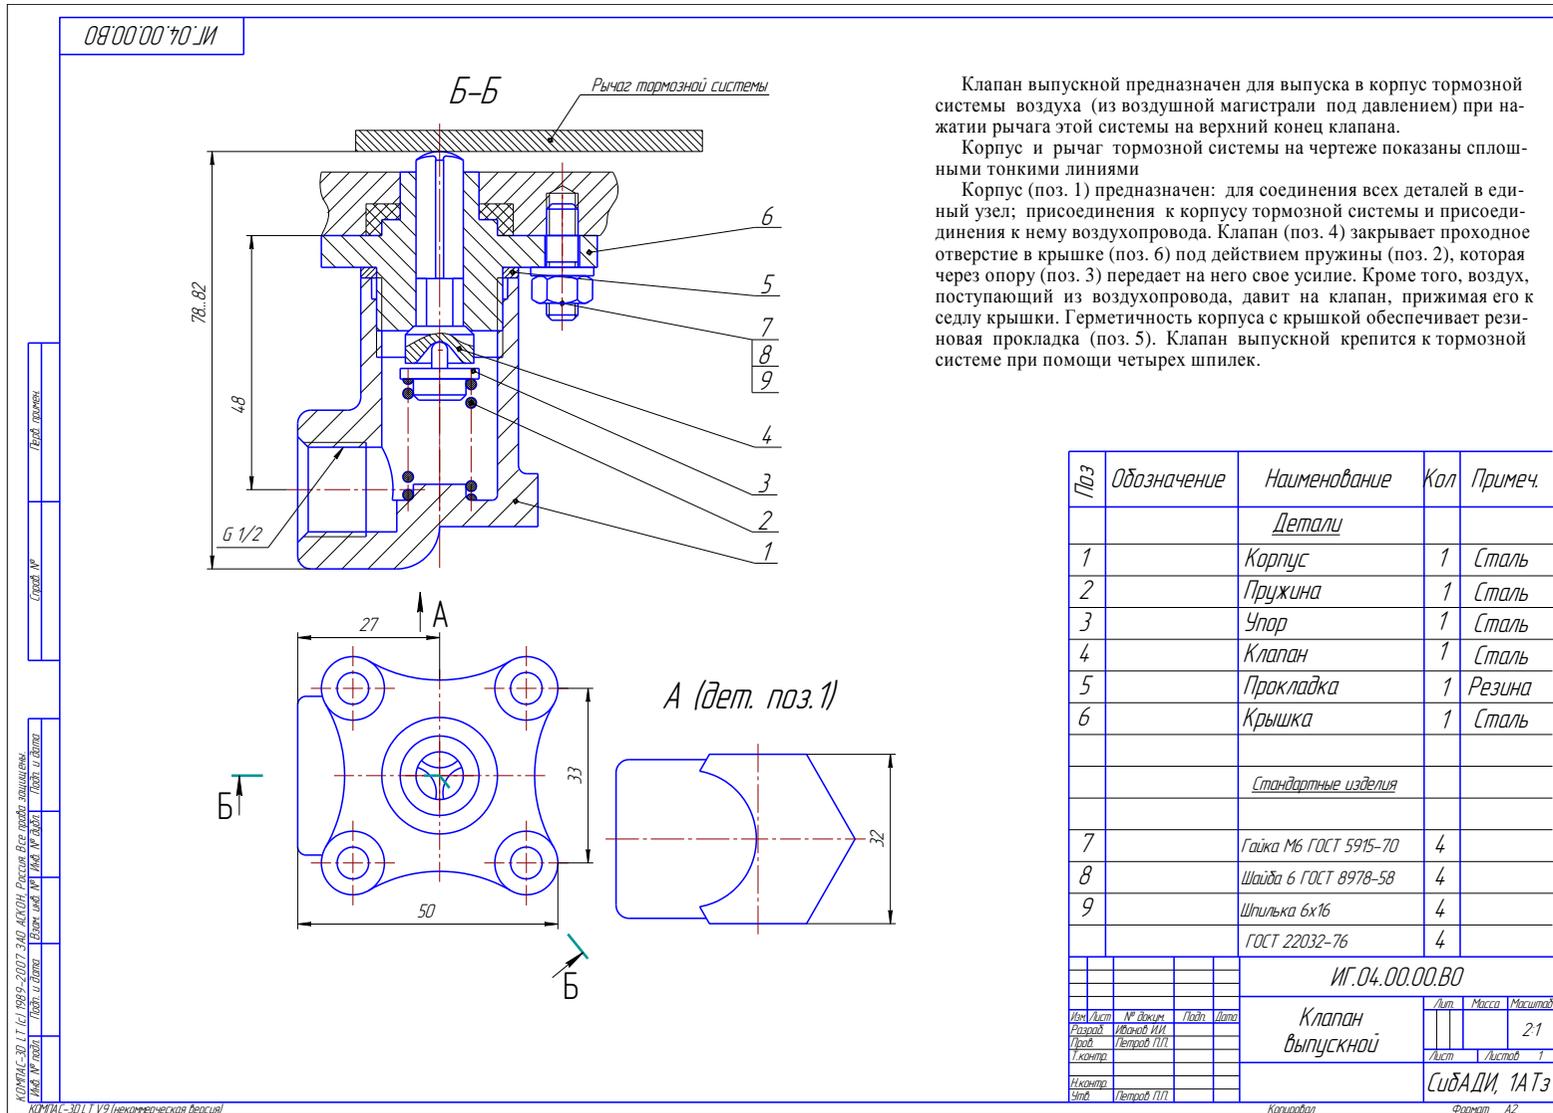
Чертеж общего вида сборочной единицы «Клапан выпускной»
